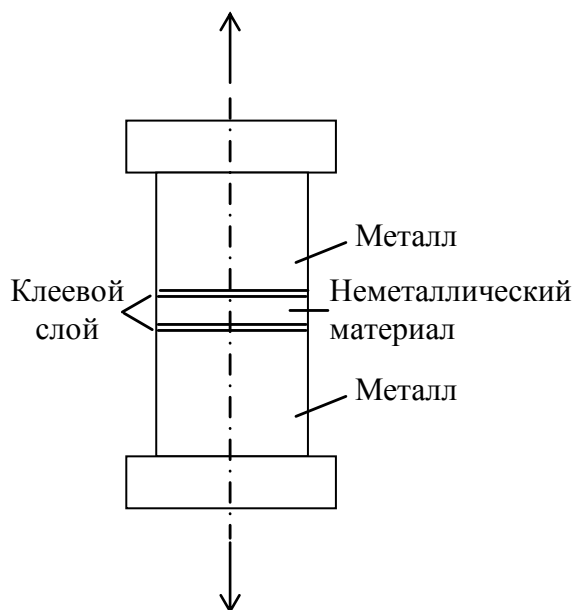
Образец для испытания клеевых соединений металла с неметаллами на равномерный отрыв
